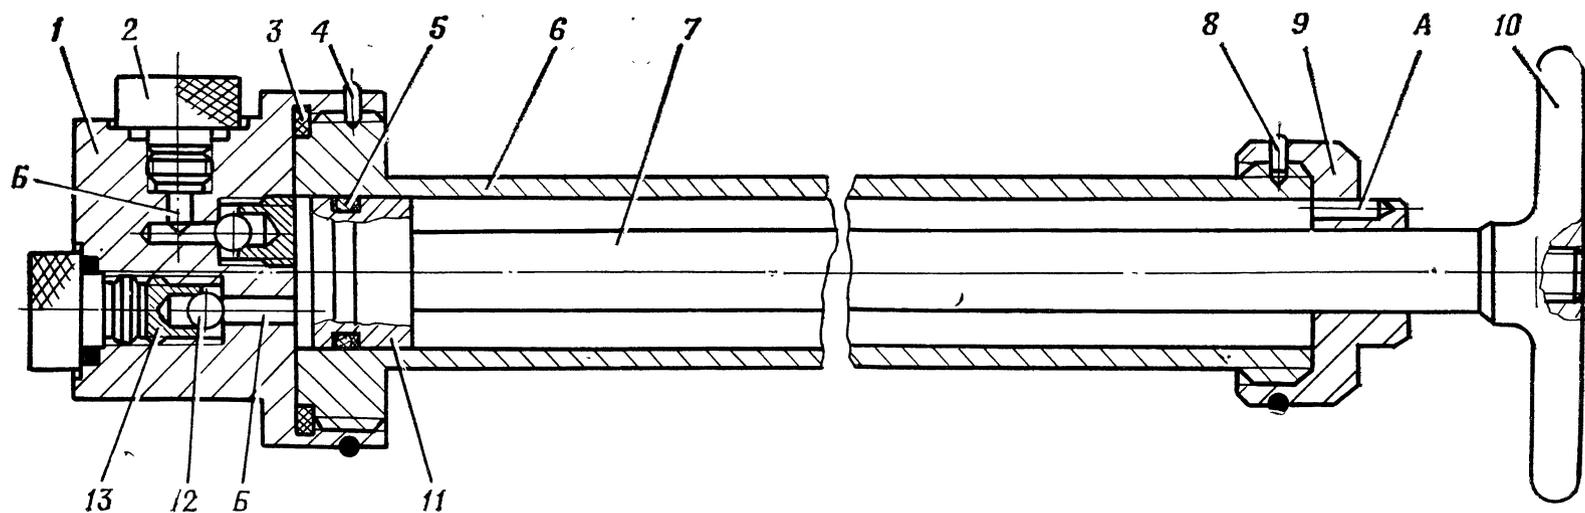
Приспособление 41.240 для заливки жидкости в тормоз отката:
